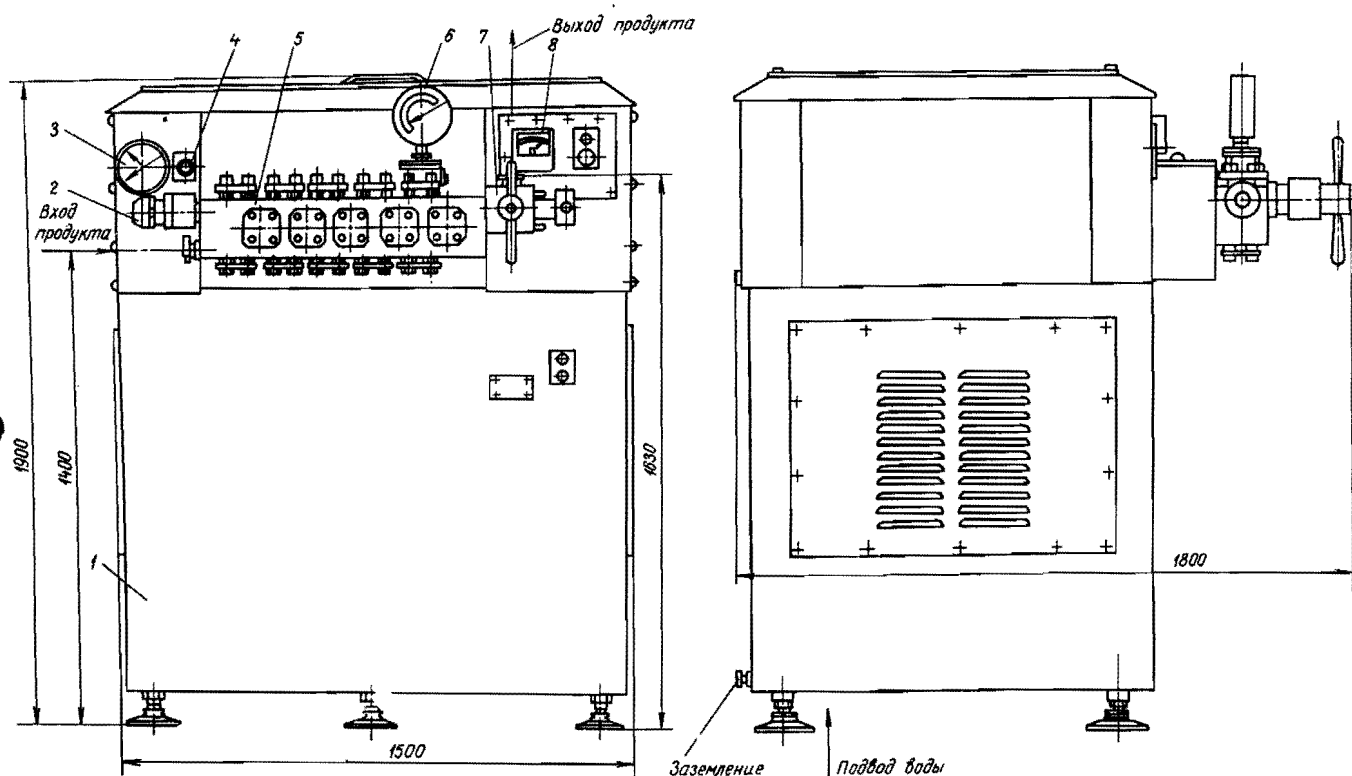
Габаритный чертеж гомогенизатора марки К5-ОГА-10:
